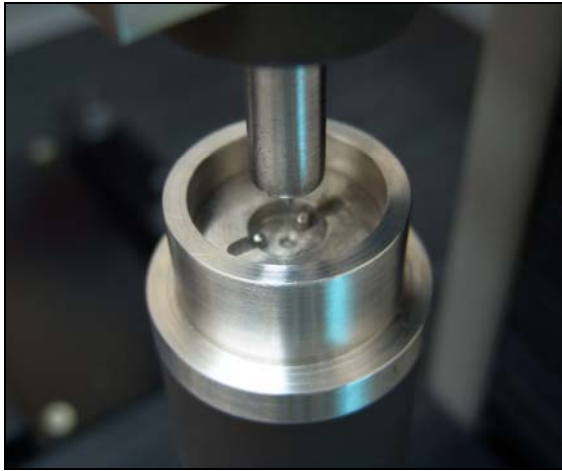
Dispositivos adaptados ao equipamento de ensaio
